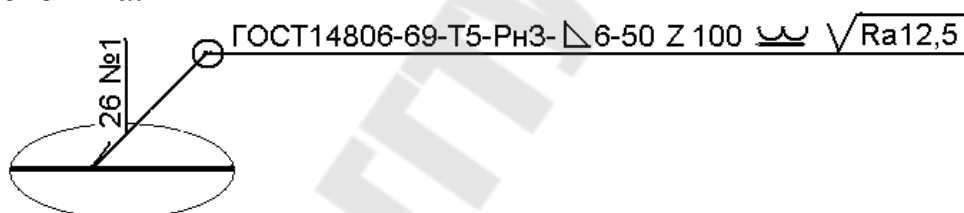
Пример условного обозначения стандартного сварного шва
